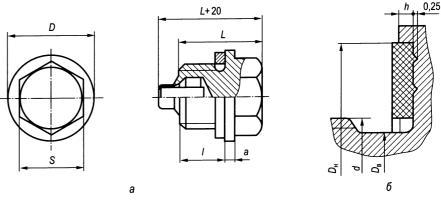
Магнитная пробка с цилиндрической резьбой для маслоспускного отверстия с плоской медной прокладкой (a) и с плоской неметаллической прокладкой (б)
